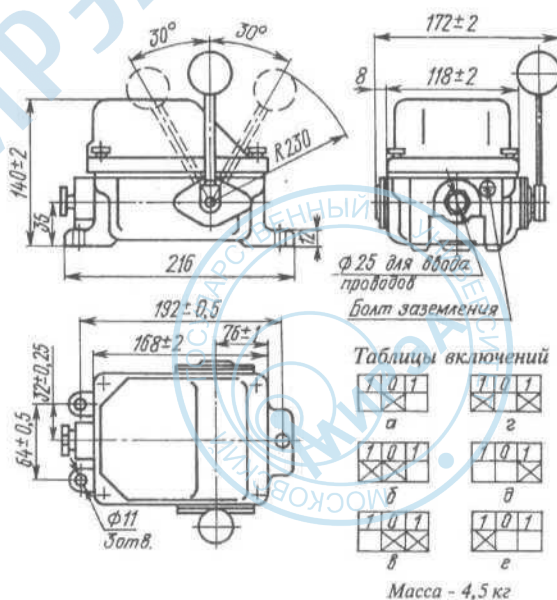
Габаритные, установочные размеры и масса выключателя типа ВУ-741
